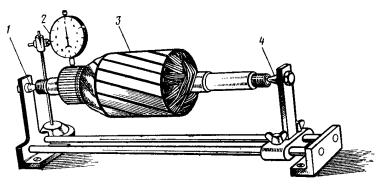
Проверка биения коллектора: 1 и 4 — центры; 2 — индикатор; 3 — якорь
